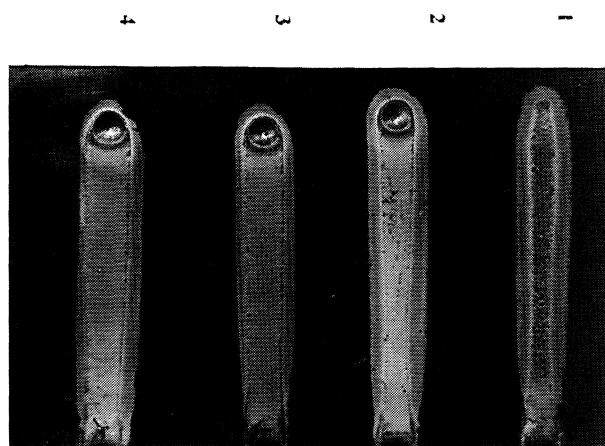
Cordones de soldadura TIG en AA7020.
